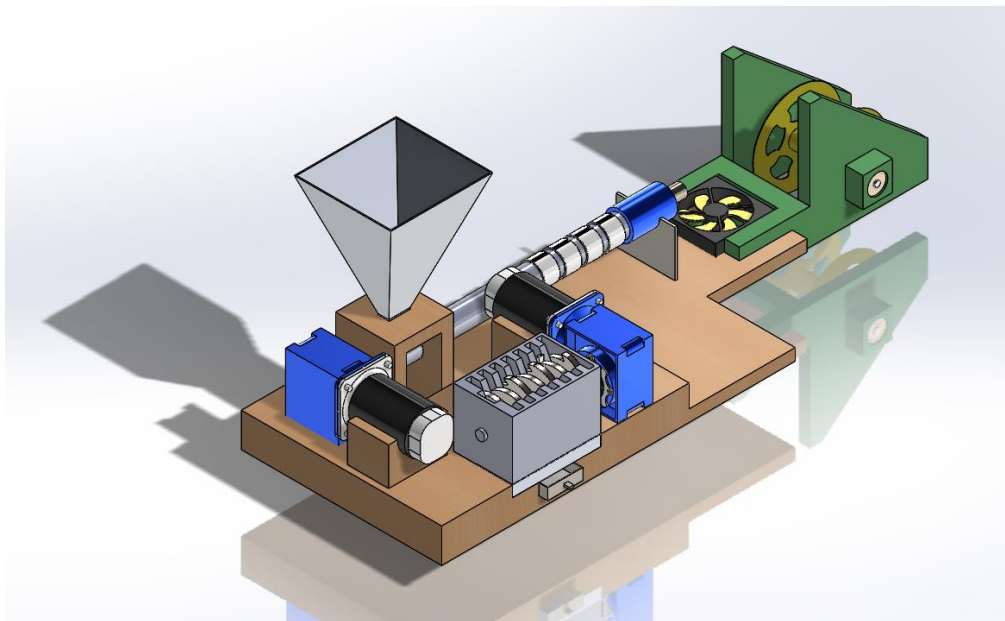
Ensamblaje final de la máquina extrusora vista 2
